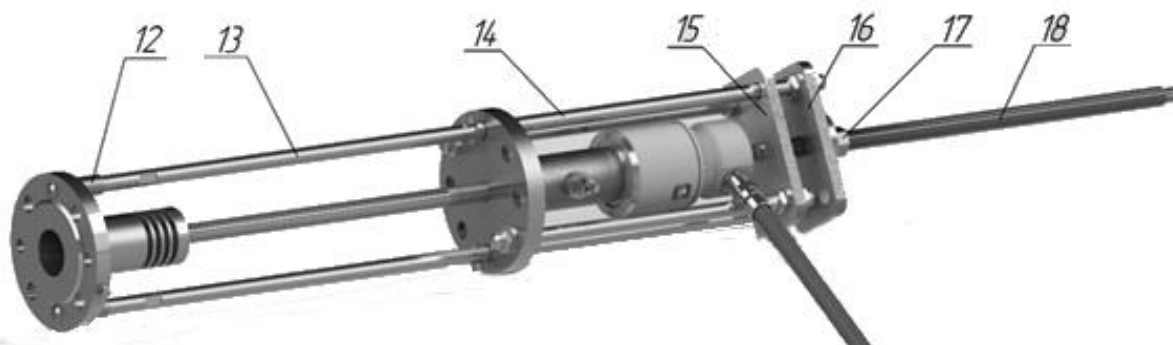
Приемопередатчик ФЛ ЛБ, с установочным приспособлением
